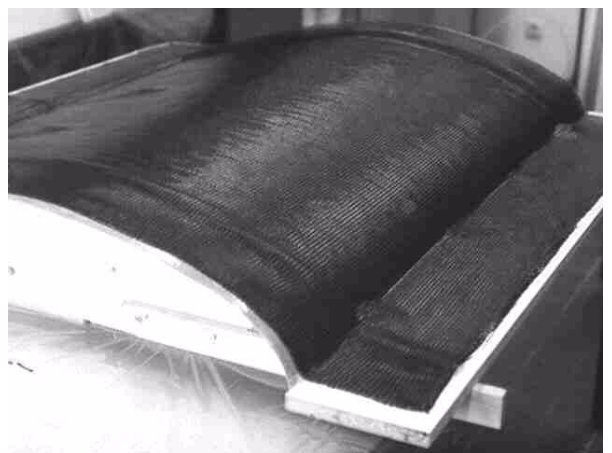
Eine zweite Schicht wird unter +/- 45° aufgebracht
